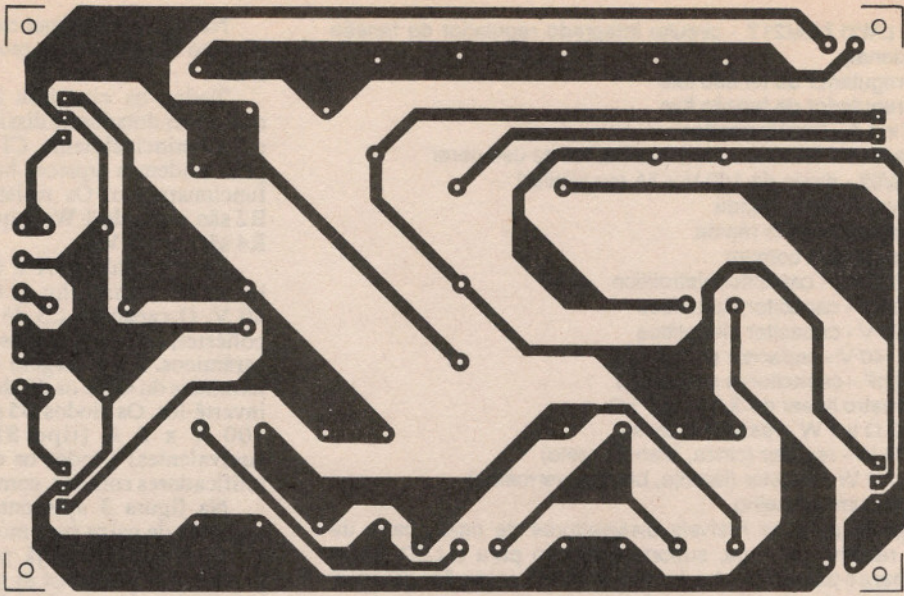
Placa de circuito impresso com a disposição dos componentes.
